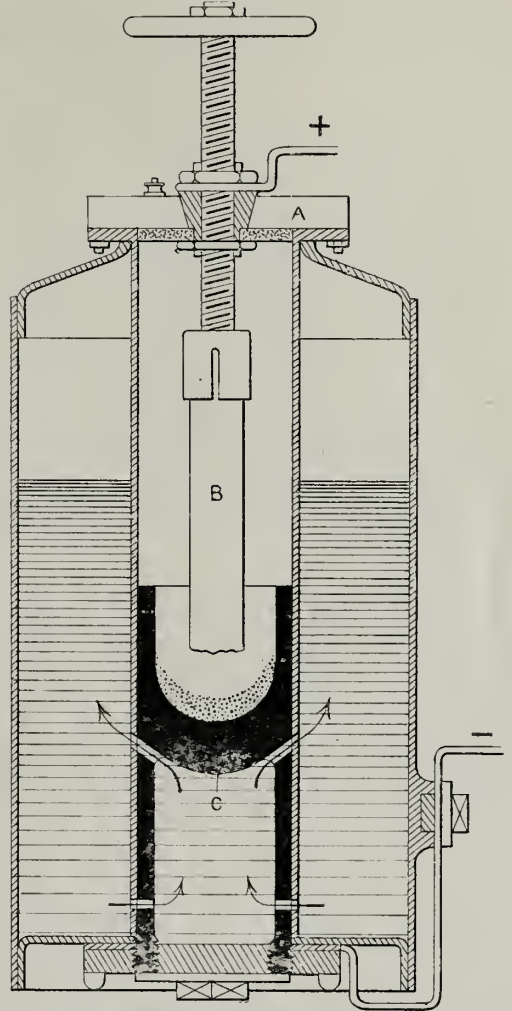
Coupe de la chaudière électrique Ougrimoff.
